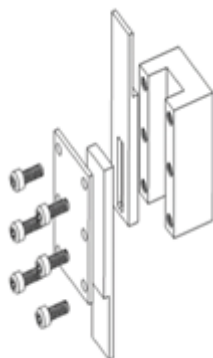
Vista explodida do dispositivo utilizado para ensaio de adesão.
